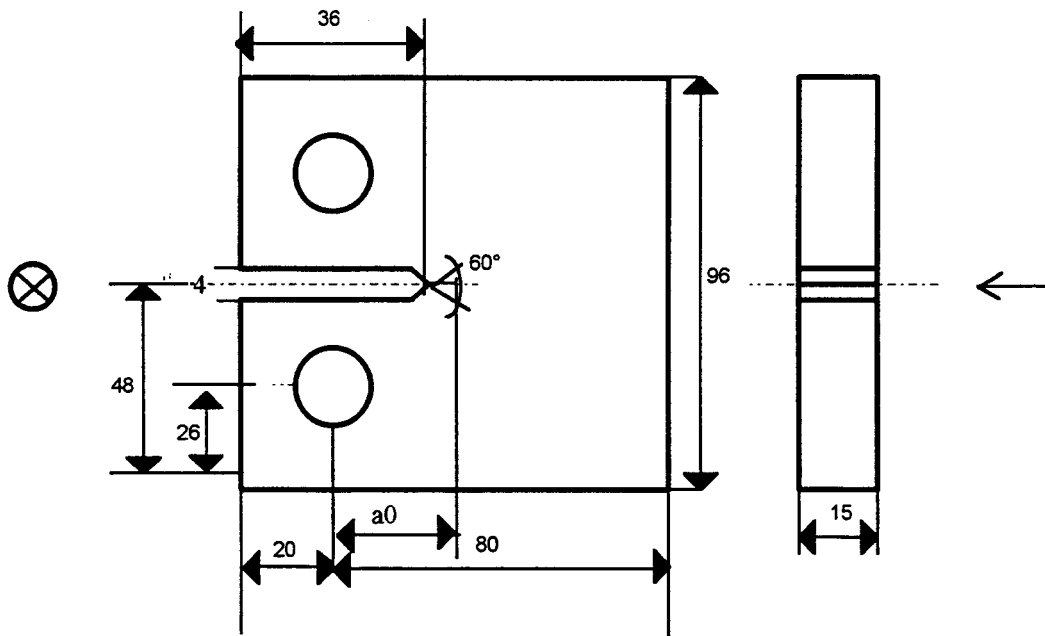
Géométrie de l'éprouvette CT-80 utilisée (en mm).
